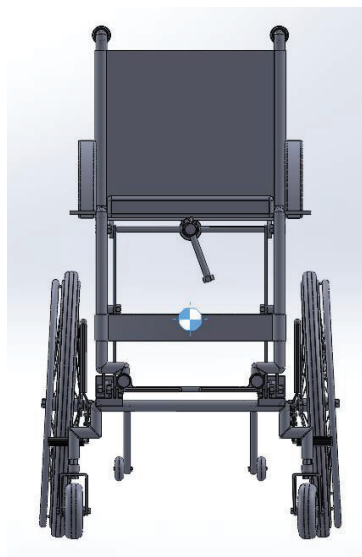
Centro de gravedad de la silla de ruedas elevada, alzado (Elaboración propia).
